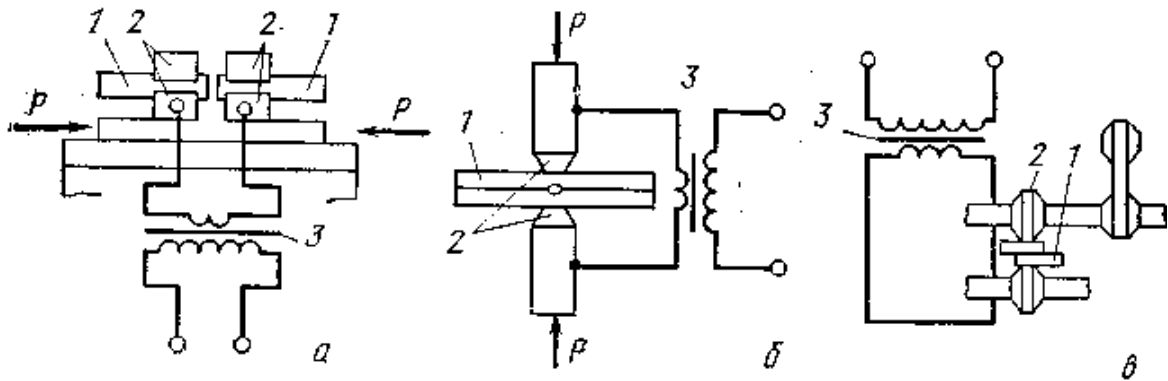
Види контактної зварювання: а – стикове; б – точкове; в – шовне; 1 – деталі, що з'єднуються, 2 – електроди, 3 – зварювальний трансформатор
